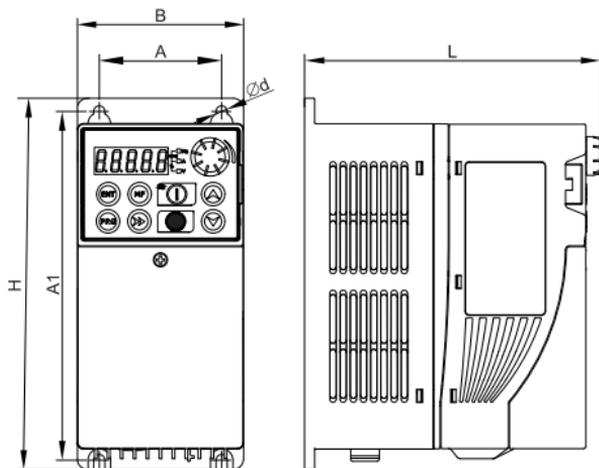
Габаритные и установочные размеры преобразователя (габарит 1)
